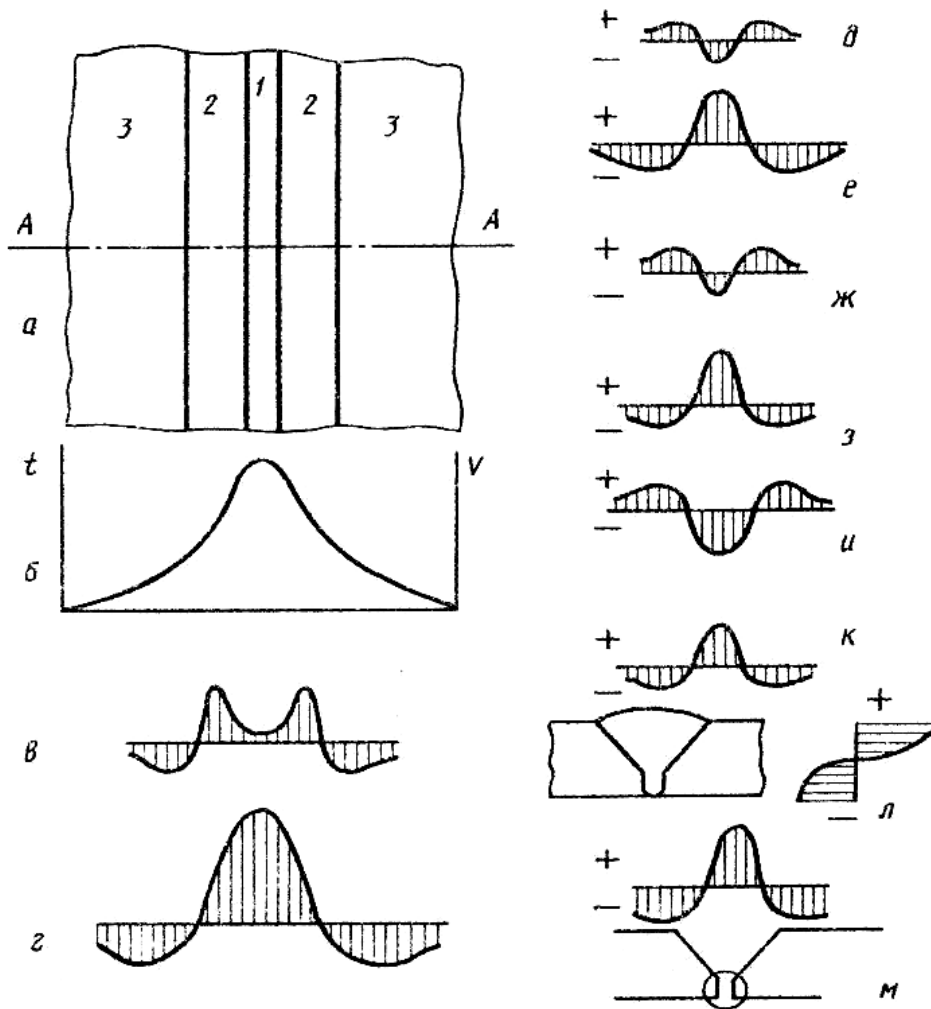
Схема возникновения временных и остаточных напряжений при сварке: 1 – сварочный шов; 2 – ЗТВ; 3 – основной металл по Л. С. Лифшицу [3]
